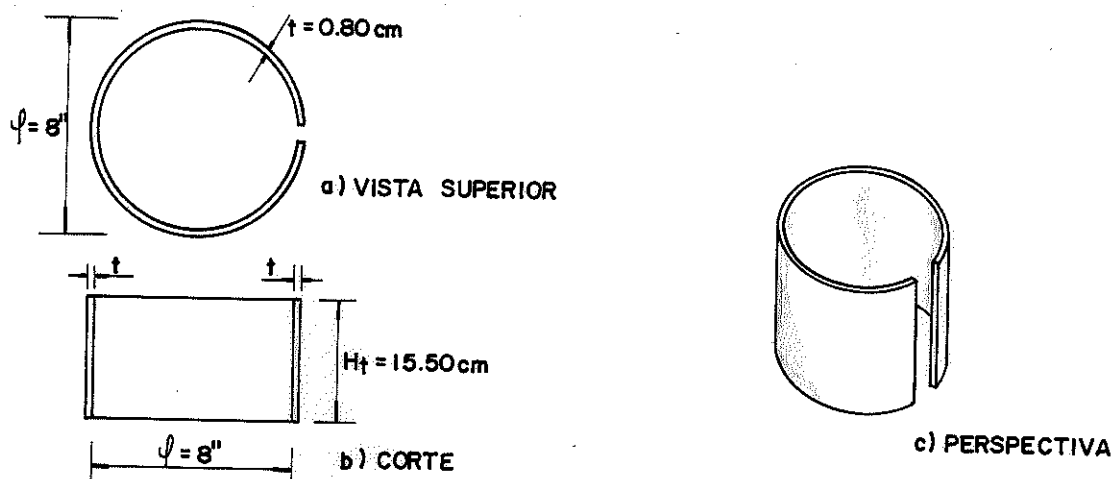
DETALHE DO ANEL METÁLICO
